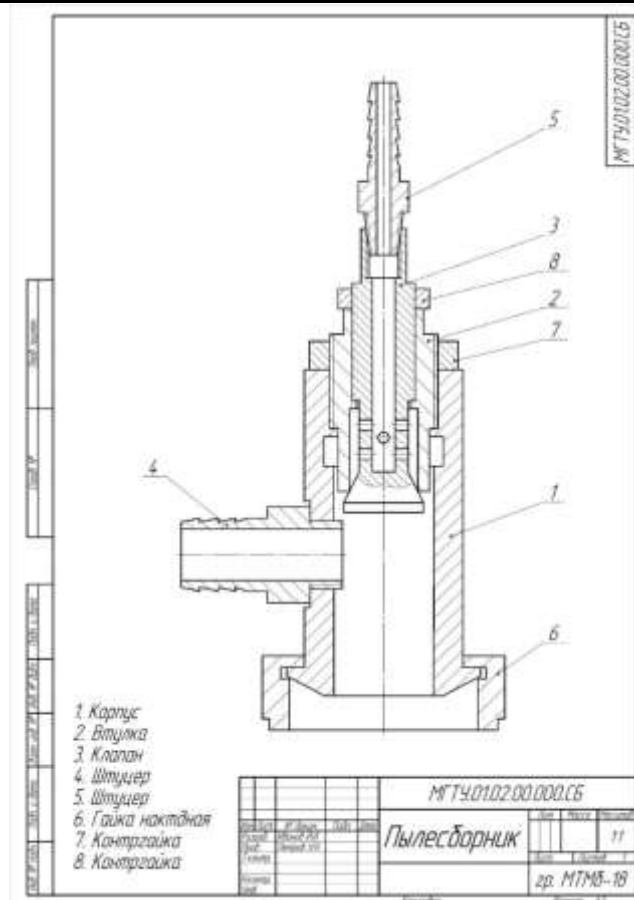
Сборочный чертеж пылесборника инжекторного, используемый в качестве метки для AR-приложения
